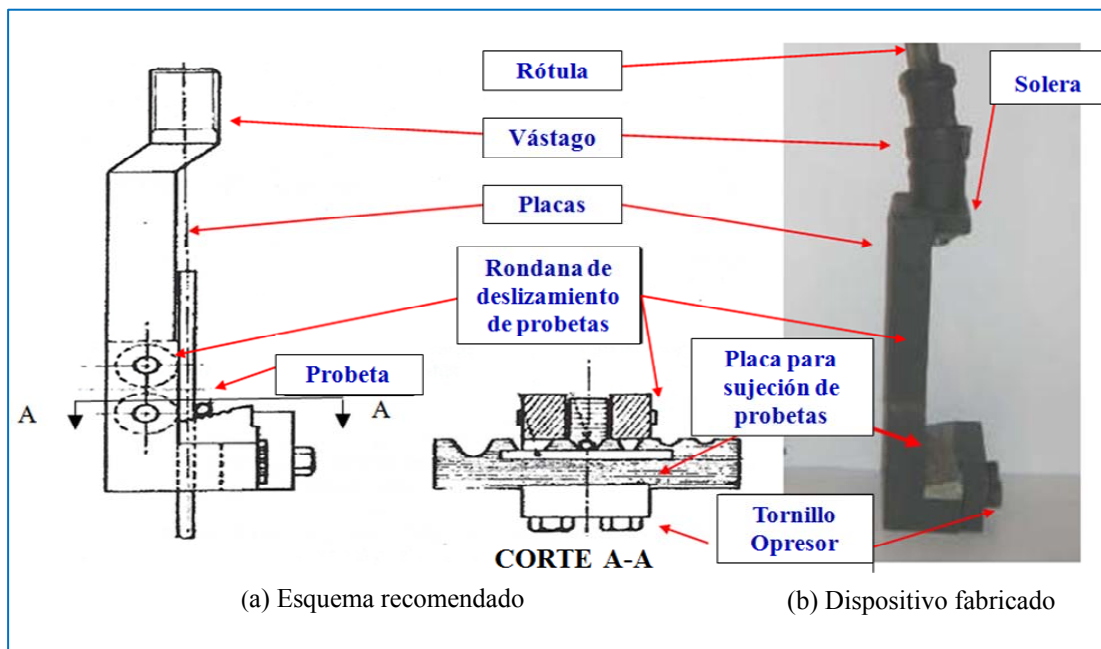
Dispositivo de cortante de soldadura
